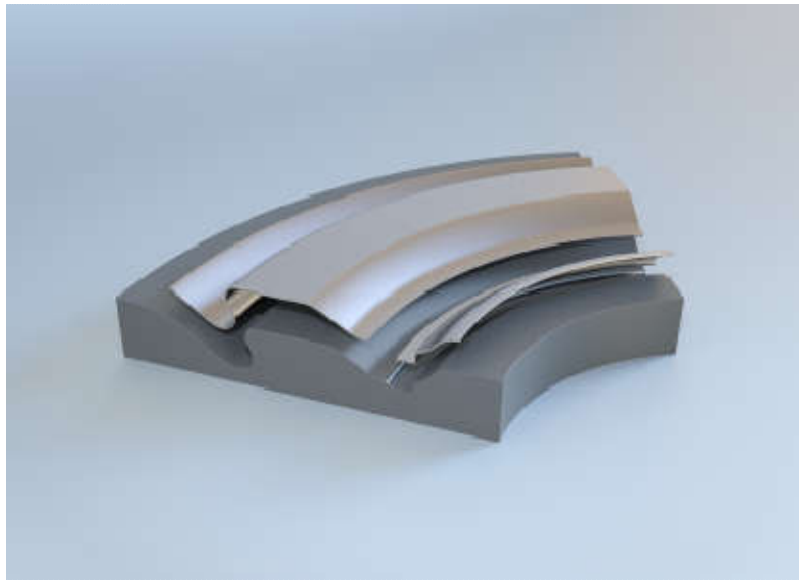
Зразок деталі виготовленої на обладнанні Flexform™
